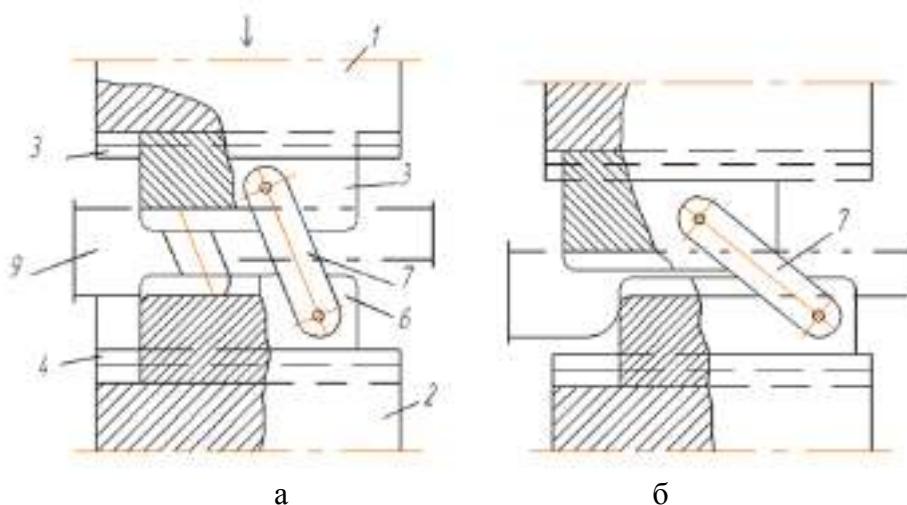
Схема инструмента для ковки с продольным сдвигом
